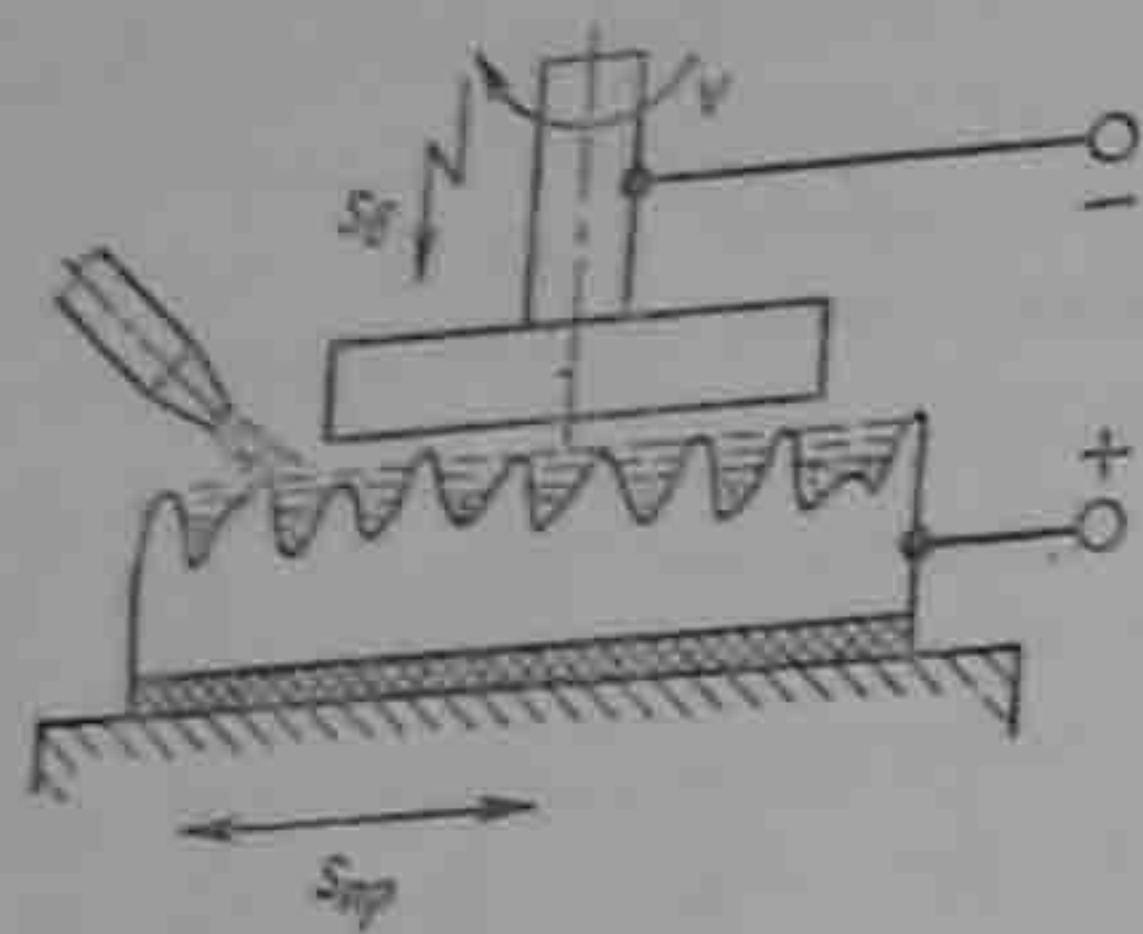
Схема анодно-механической обработки плоской поверхности
